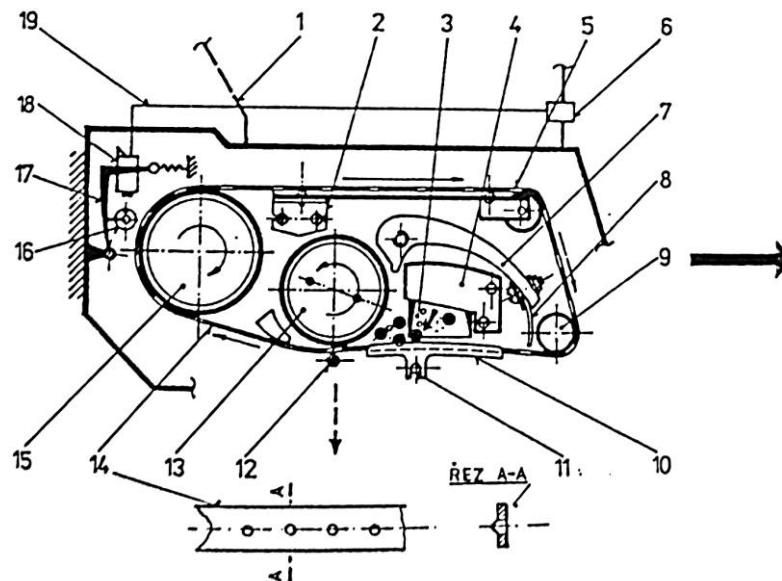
Výsevní ústrojí s horizontální osou rotace [4];
